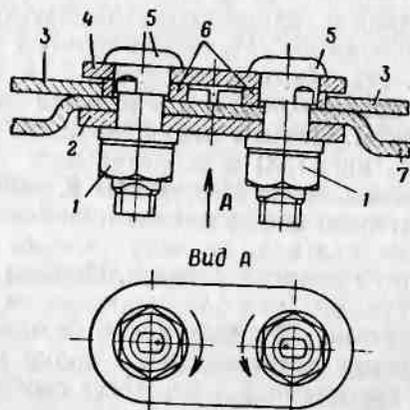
Положение установочных пальцев колодок при сборке тормоза:
